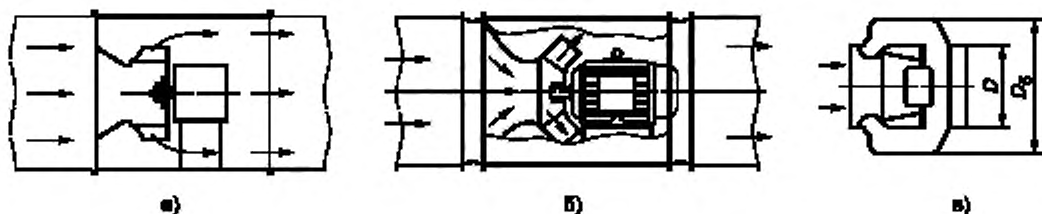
Канальные круглые вентиляторы с цилиндрическим корпусом с радиальным [а)] и диагональным [б)] рабочим колесом, с торообразным корпусом с радиальным рабочим колесом [в)]
